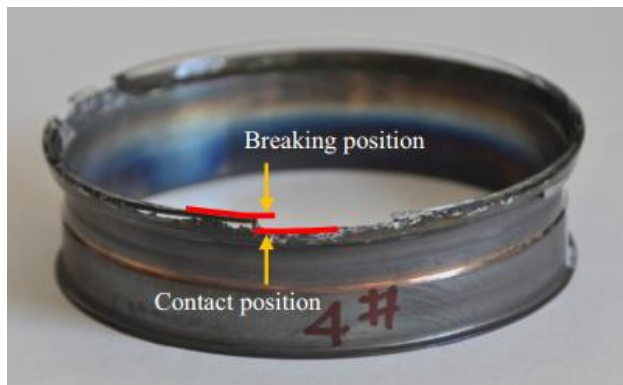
Fractura de la soldadura vidrio metal [76].
